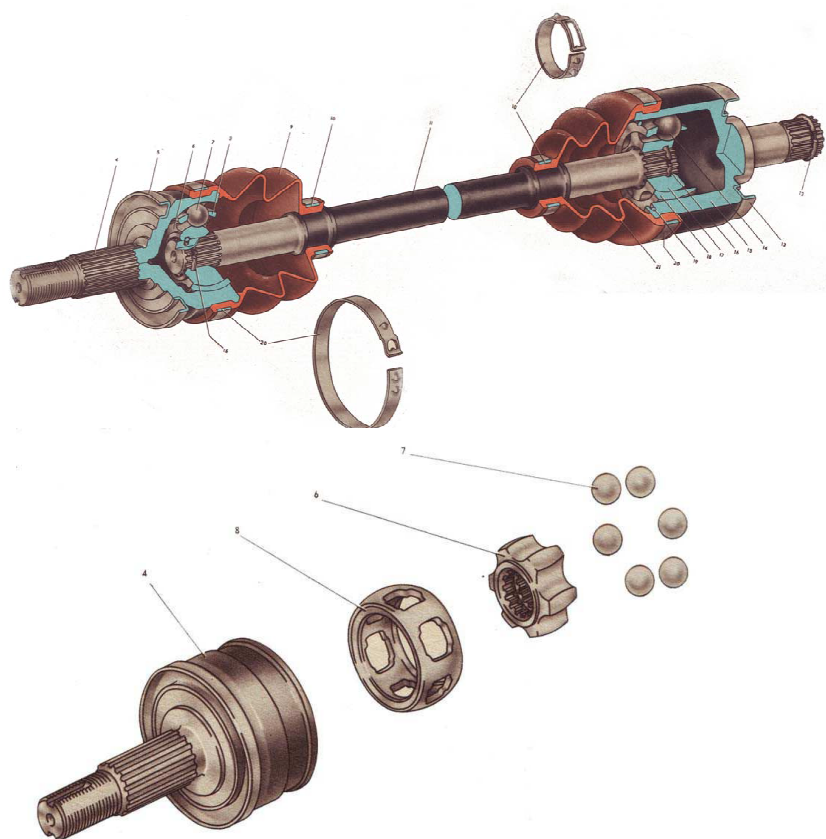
Привод к ведущим и управляемым колесам легкового автомобиля с шарнирами равных угловых скоростей»[4]
